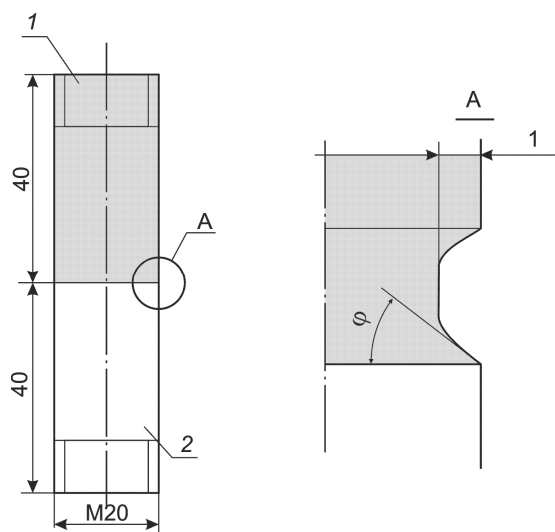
Образец для испытаний (1 — ПММА, 2 — латунь)
